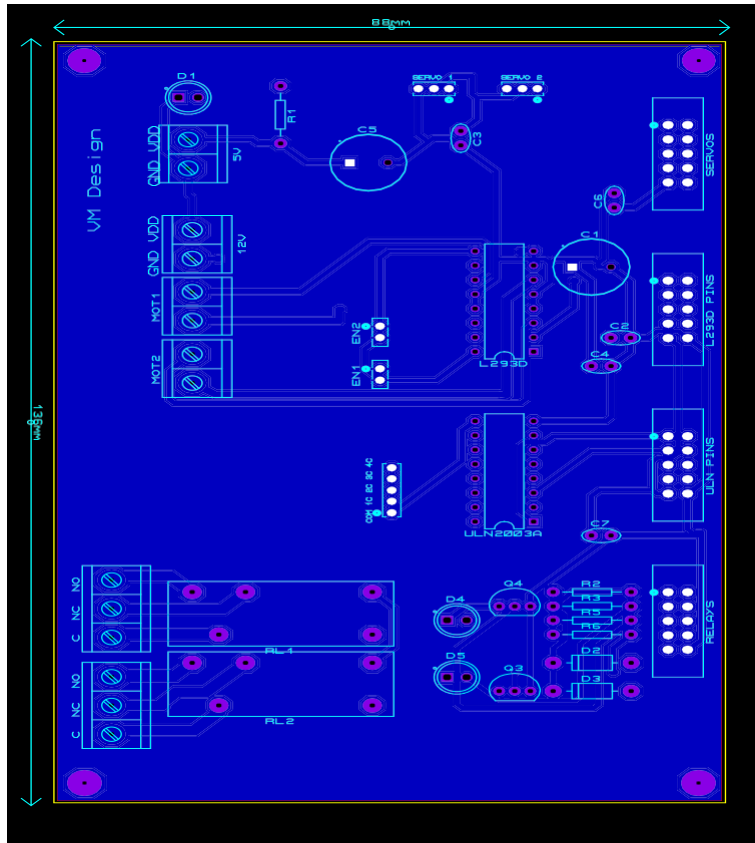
schéma PCB de la carte de commande de moteurs.
